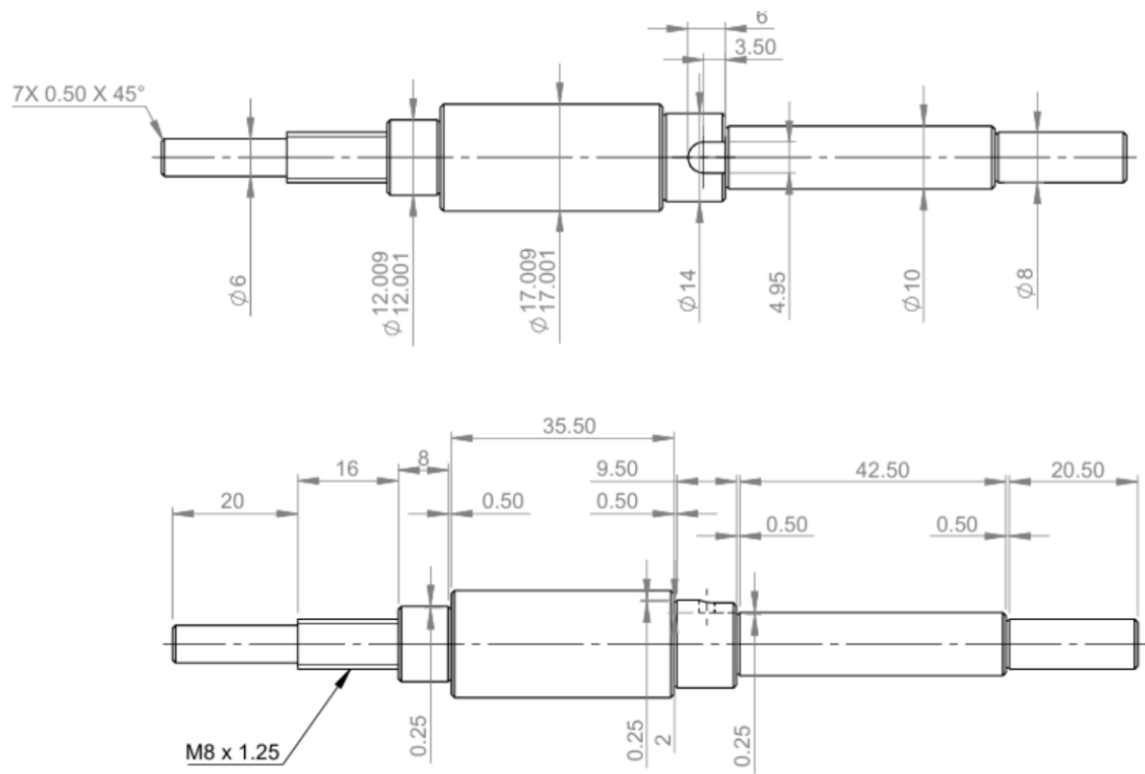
Engineering Drawing: Bearing Mounting
